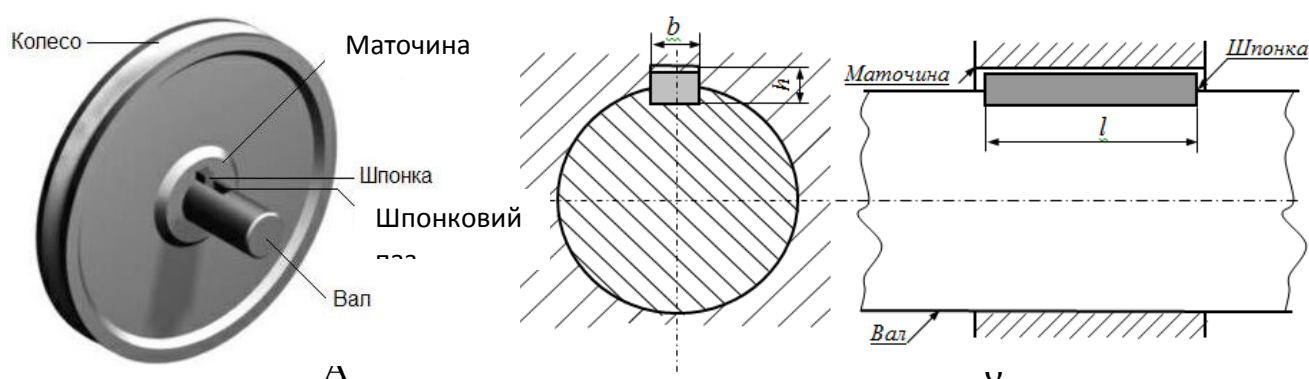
Шпонкове з'єднання: а - деталі; б - зображення
